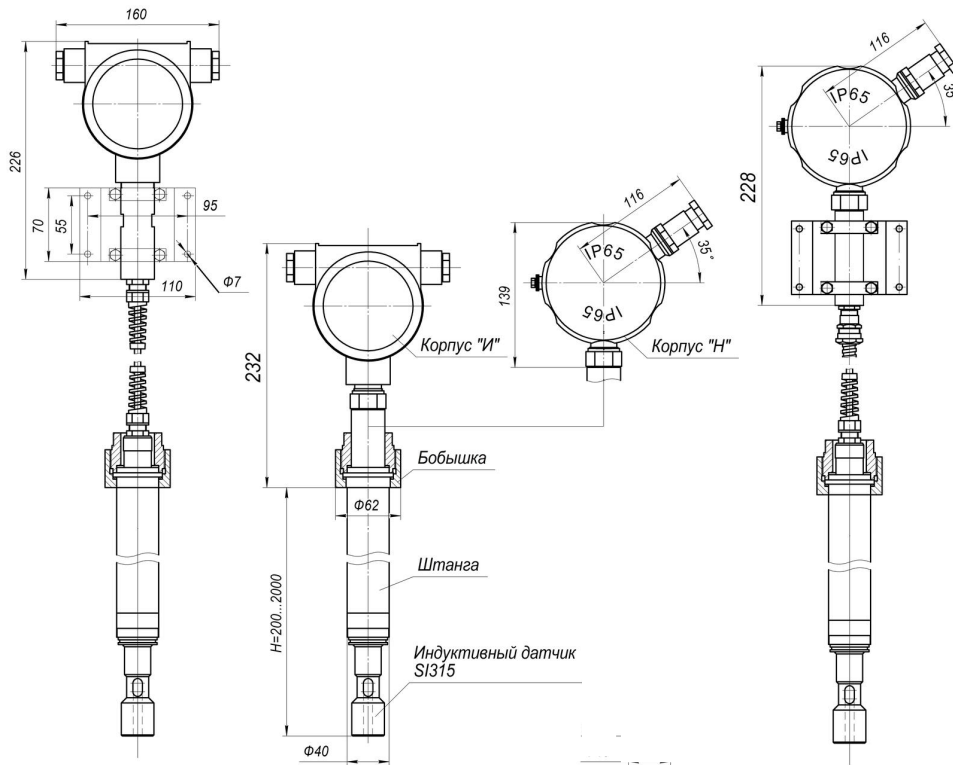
Габаритные и монтажные размеры первичного преобразователя с погружной арматурой АПП-2.2 с бобышкой и индуктивным датчиком SI-315
